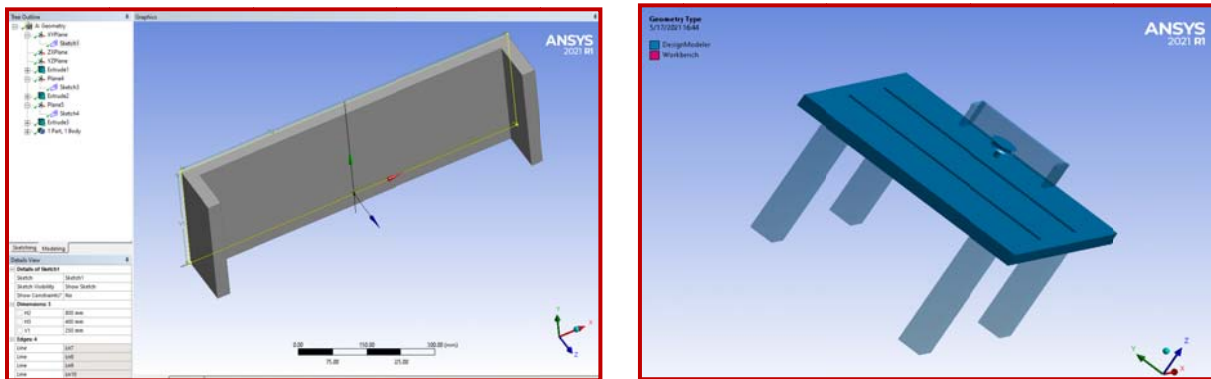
(a) couvercle, (b) Montage d'un couvercle de protection.
